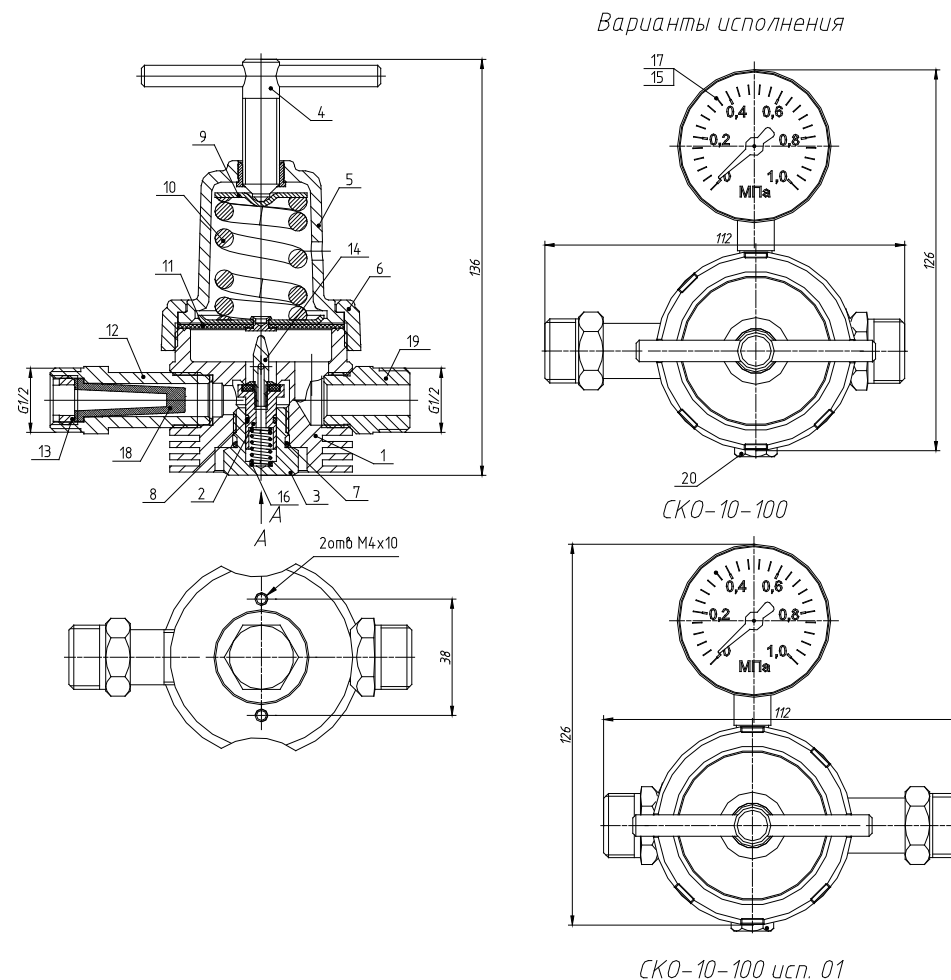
Редуктор сетевой кислородный одноступенчатый
